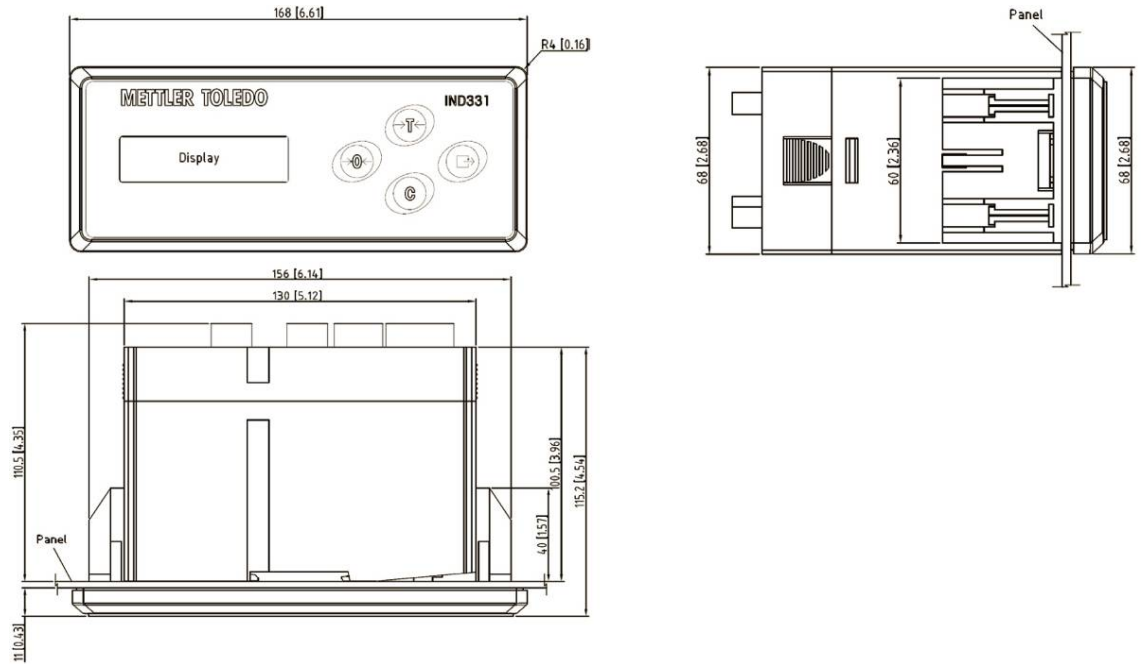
Dimensões do gabinete do IND331 para montagem em painel
